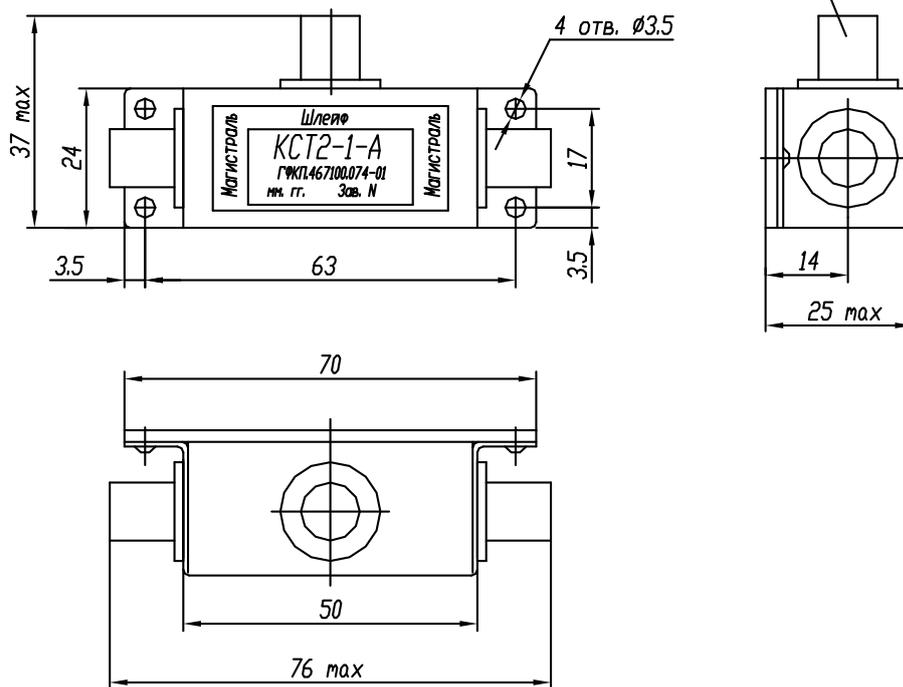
Габаритный чертеж коробки соединительной КСТ2-1
